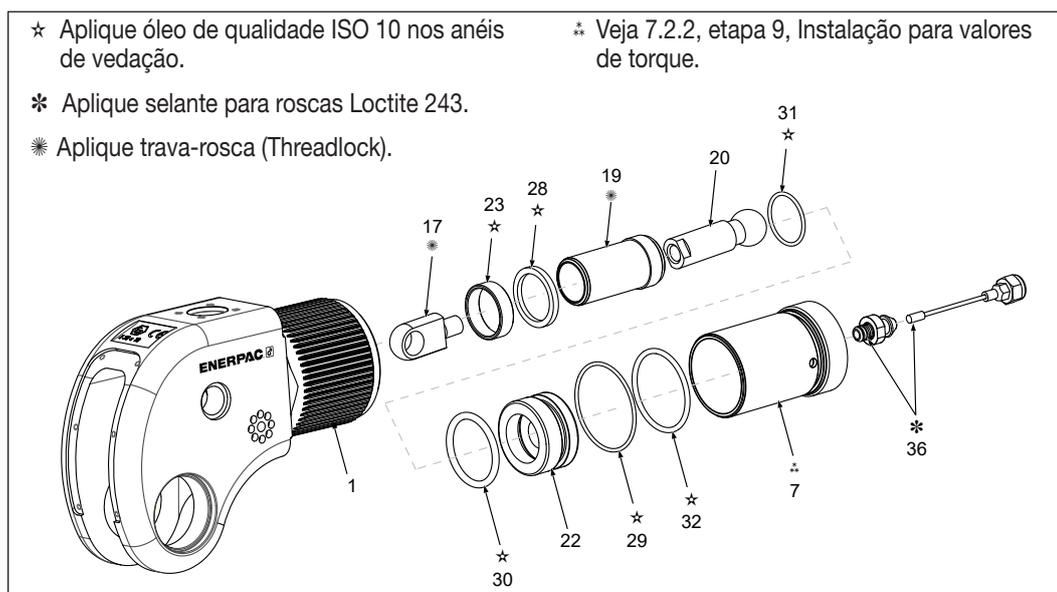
Pistões DSX1500, DSX3000 e DSX5000 explodidos
